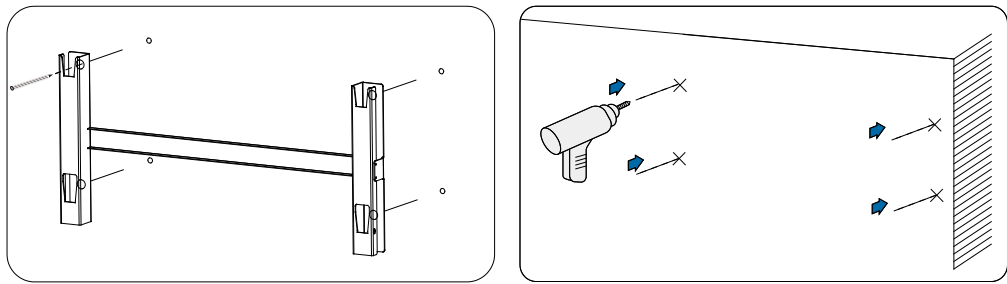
Trapanatura dei fori sulla parete di montaggio
